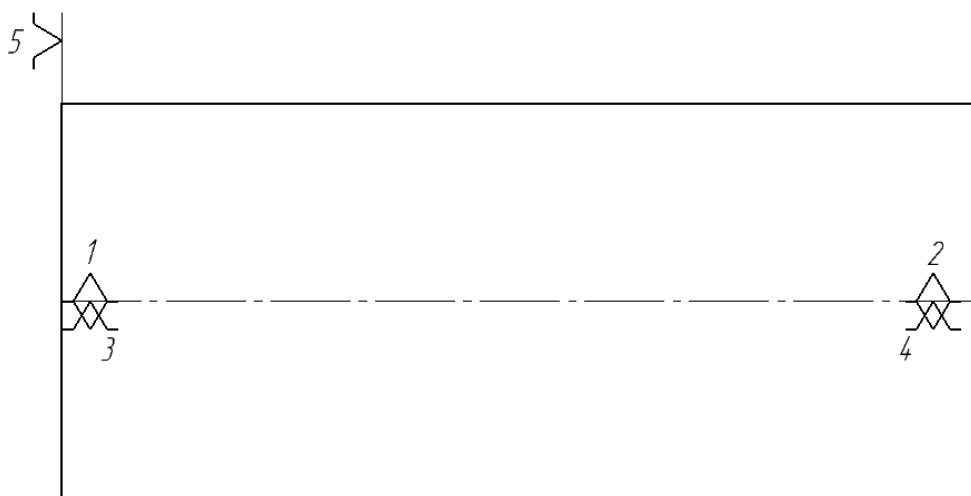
Теоретична схема базування деталі «Вал-шестерня»
